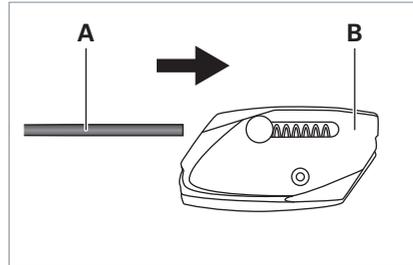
Fijación del soporte del cable metálico en el cable metálico.
